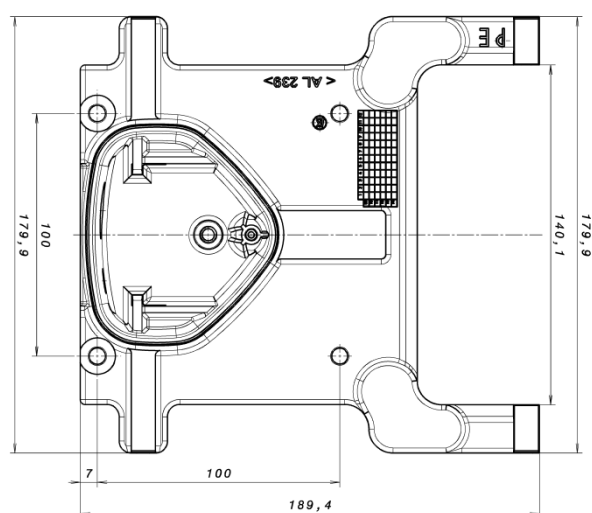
Bohrbild Standard-Wand-Adapterplatte BG C
